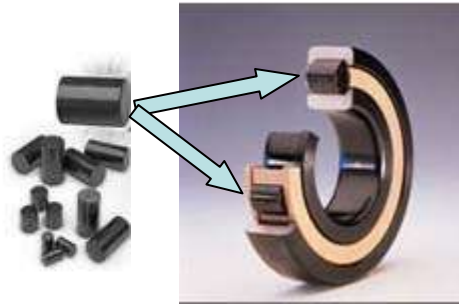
Rodillos empleados en la fabricación de rodamientos
